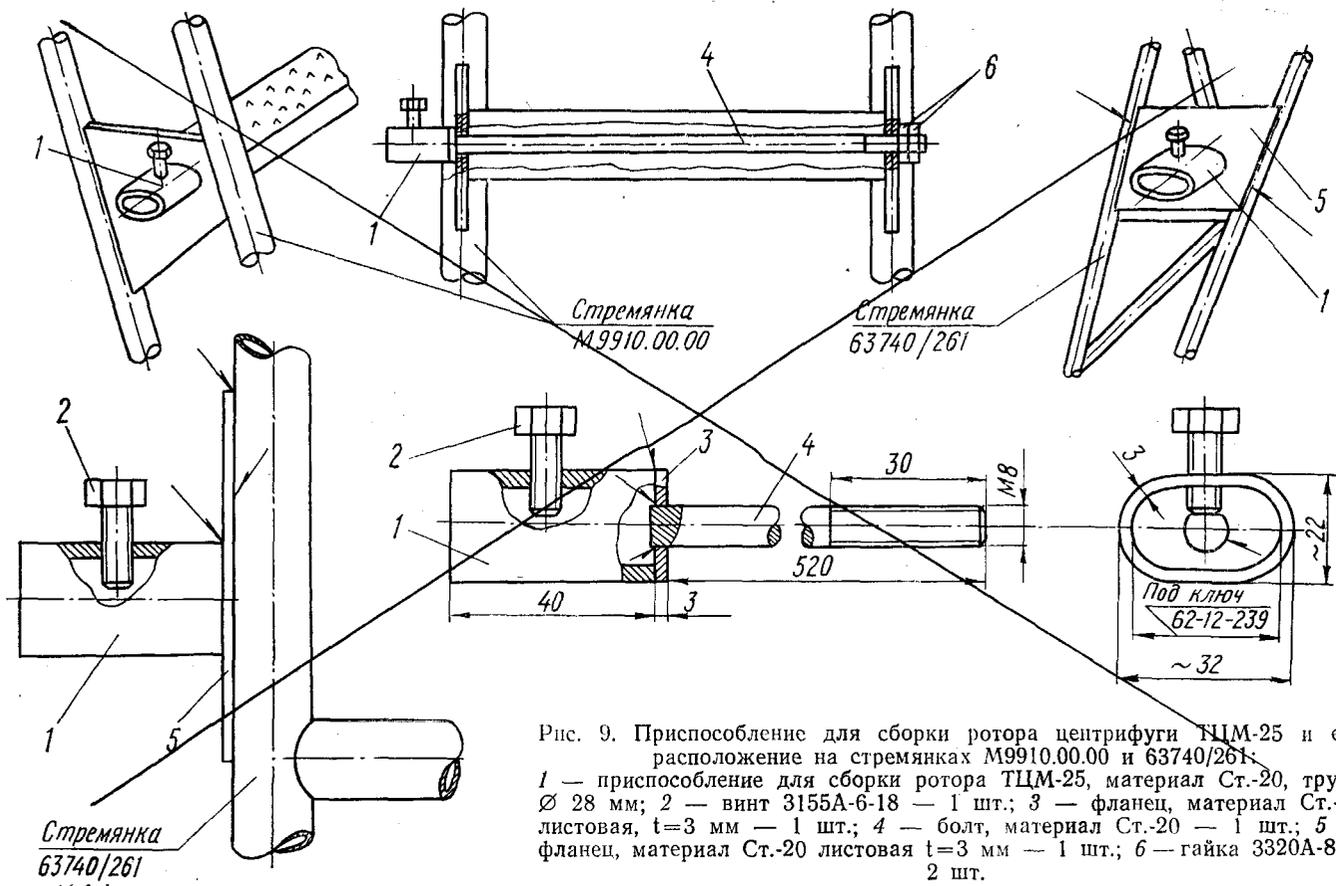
Приспособление для сборки ротора центрифуги ЦМ-25 и его расположение на стремянках М9910.00.00 и 63740/261:
